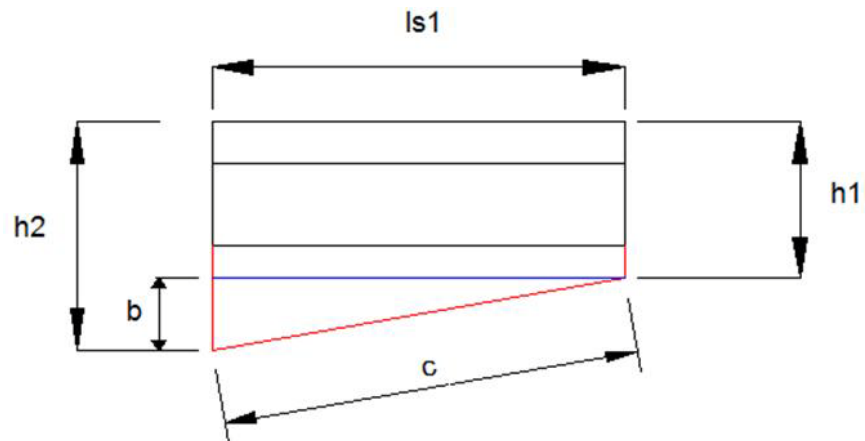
Dimensiones de la cámara de secado con aislamientos
